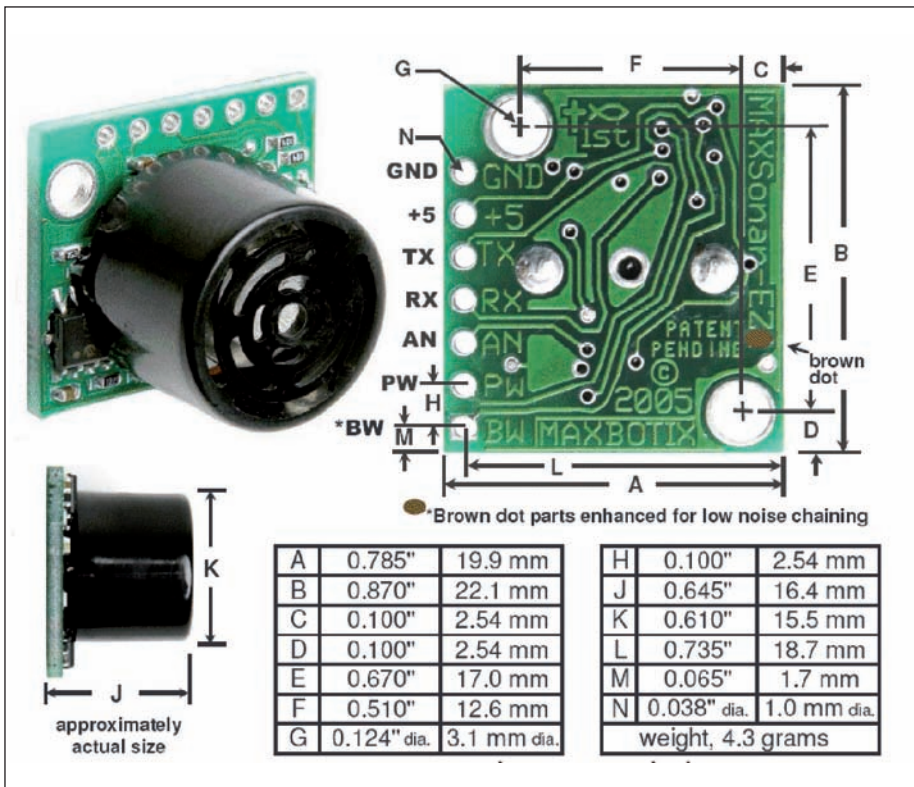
piedinatura e dimensioni del sensore EZ1.
